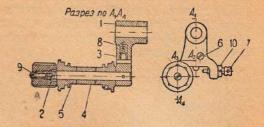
Каретка подающего и успокаивающего барабанов: 1—вилка; 2—рукоятка; 3—штифт; 5—ролики; 6—винт; 8—пружина; 9—винт; 10—контргайка
